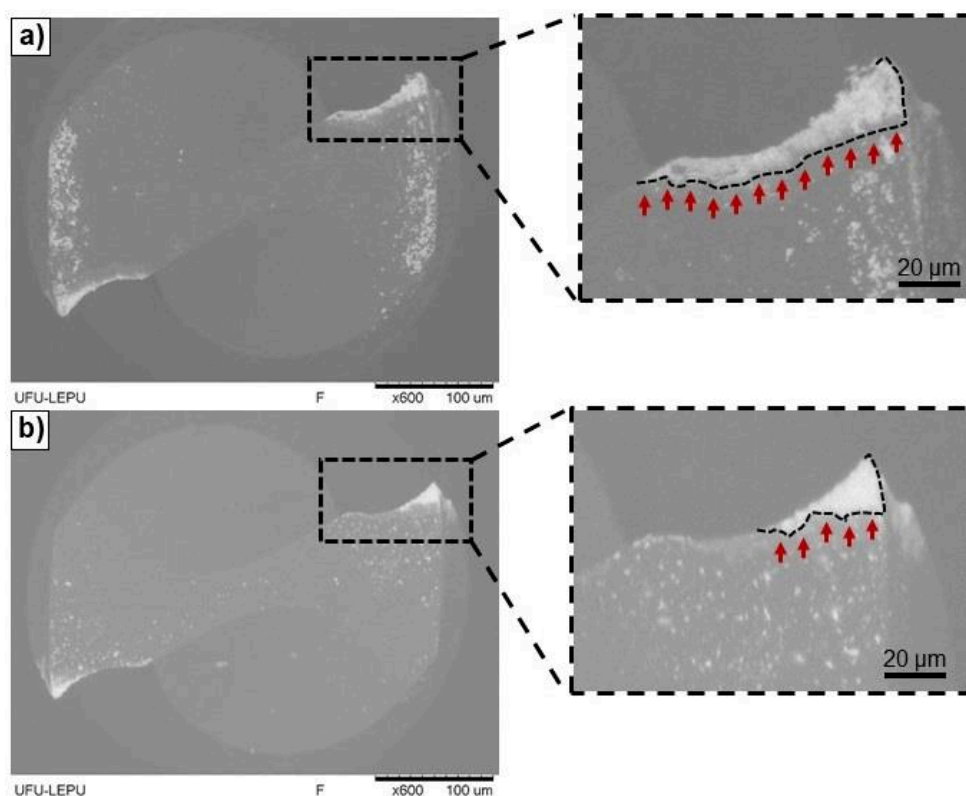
Desgaste de flanco na superfície secundária de folga das ferramentas com revestimento DLC, em (a) usinagem a seco e (b) usinagem utilizando MQL.
